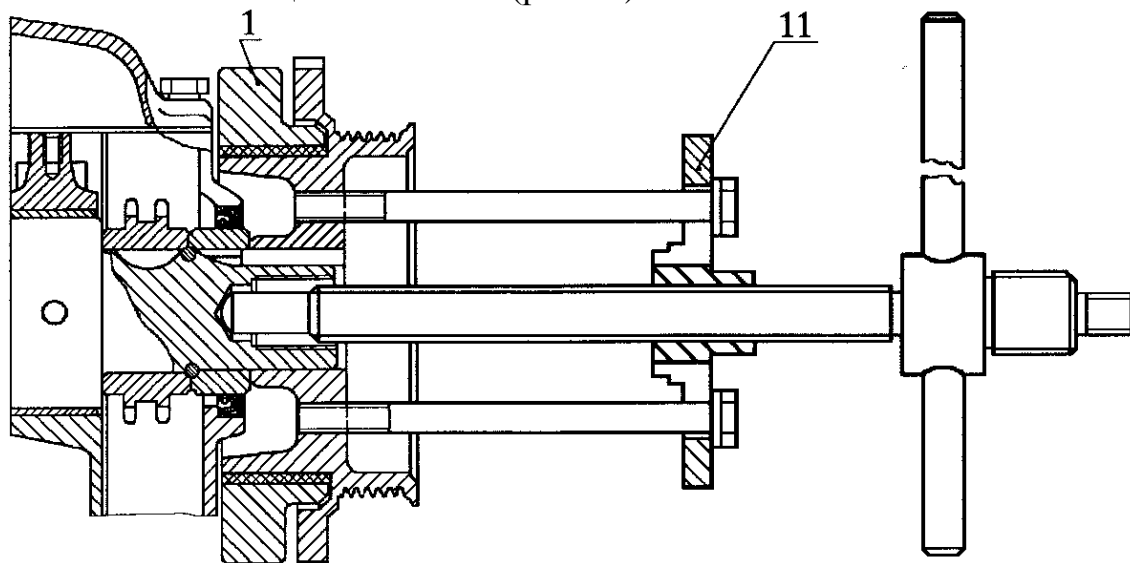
Снятие шкива коленчатого вала с помощью съёмника:
